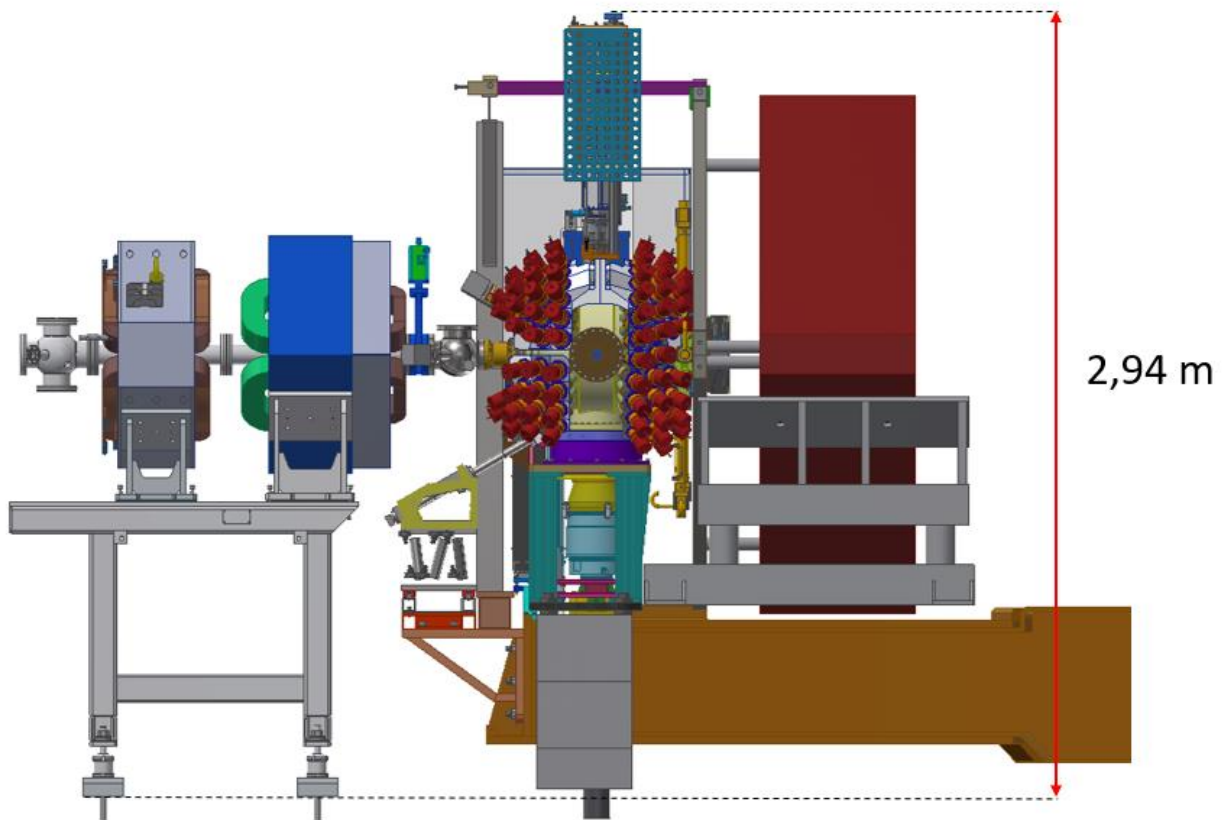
Vista laterale della camera e degli elementi limitrofi, la linea di fascio giunge da sinistra. Una volta montato il sistema, con le guide estese la piastra di finecorsa dista dal pavimento 2,92 m.
